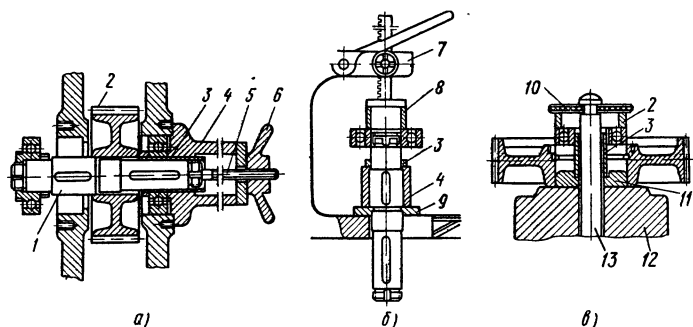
Схемы запрессовки деталей с помощью механических приспособлений:
